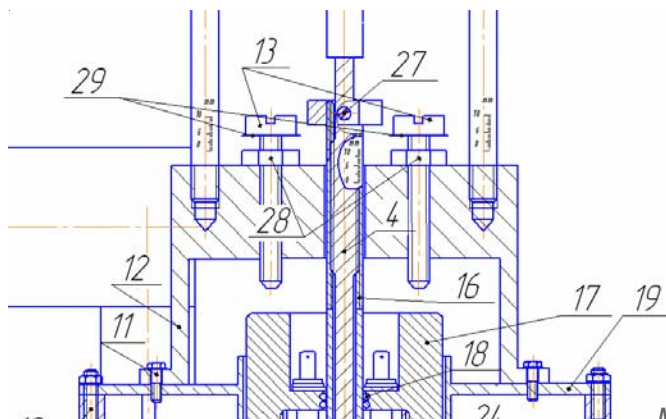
Регулировка подачи порошковых материалов винтами 13
